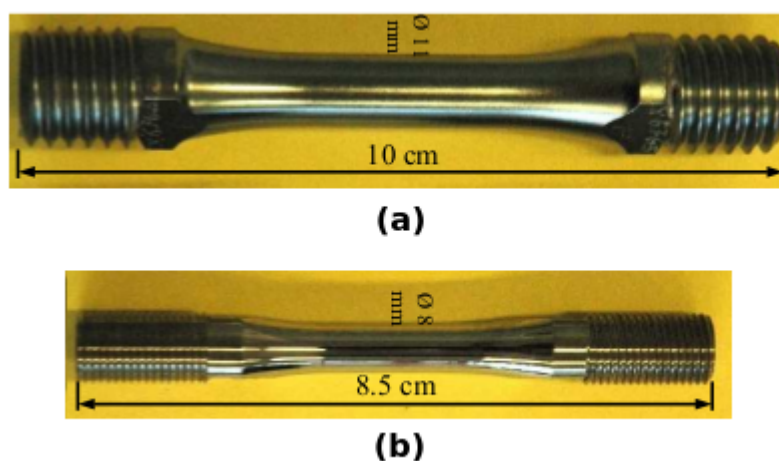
Éprouvettes utilisées pour les essais de fatigue thermo-mécanique : (a) éprouvette tubulaire TMF (b) éprouvette tubulaire TMF courte [Sallot, 2012]
